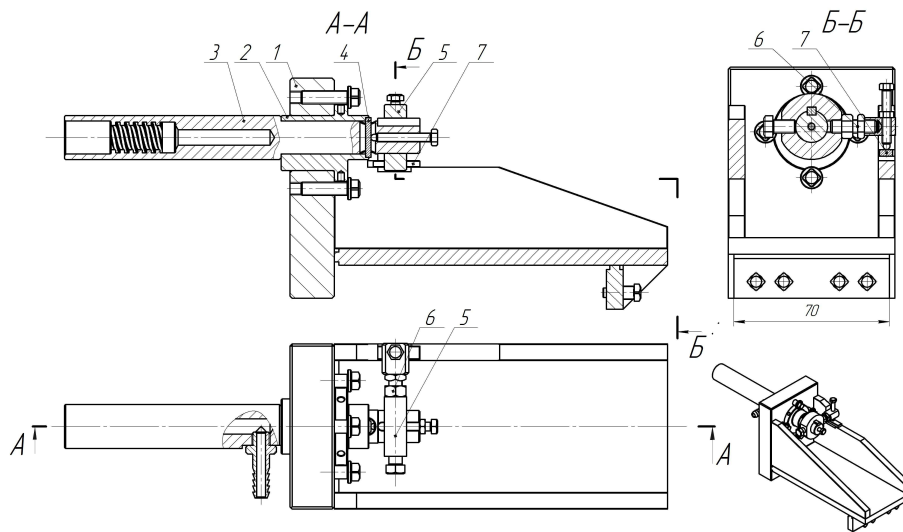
Пристрій для вимірювання силових характеристик процесу різання при обробленні внутрішніх циліндричних поверхонь
